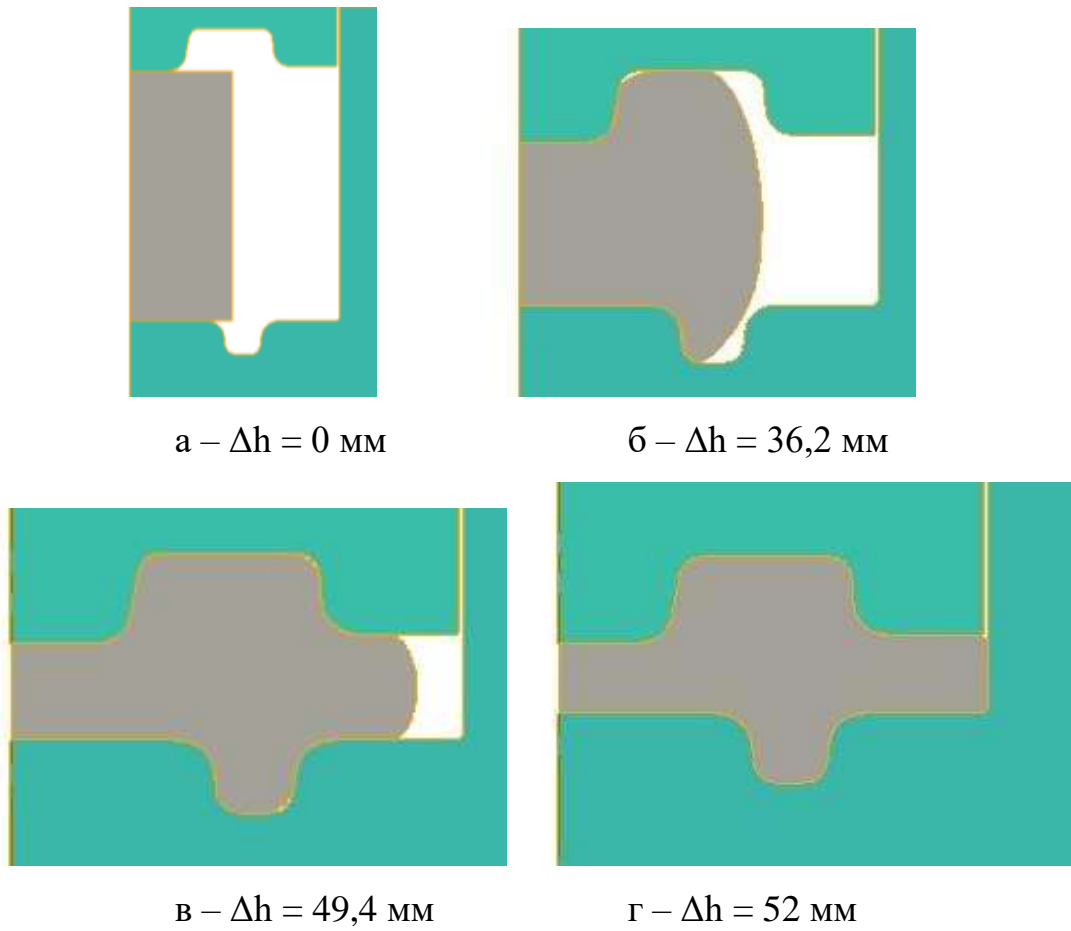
Формоизменение металла при штамповке фланца из цилиндрической заготовки
